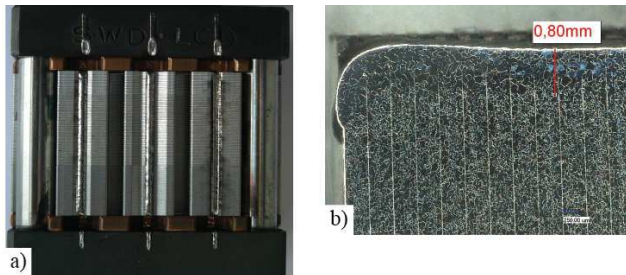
a) Draufsicht auf Laser geschweißten Probekörper und b) Längsschliffbild einer Schweißnaht im Elektroblech M270-50 A mit Dünnschicht-Lackierung
